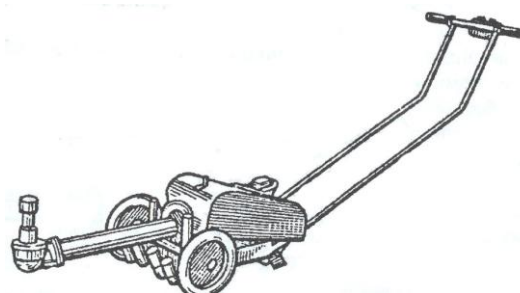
Гайковёрт для гаек стремянок рессор модель И 319.
